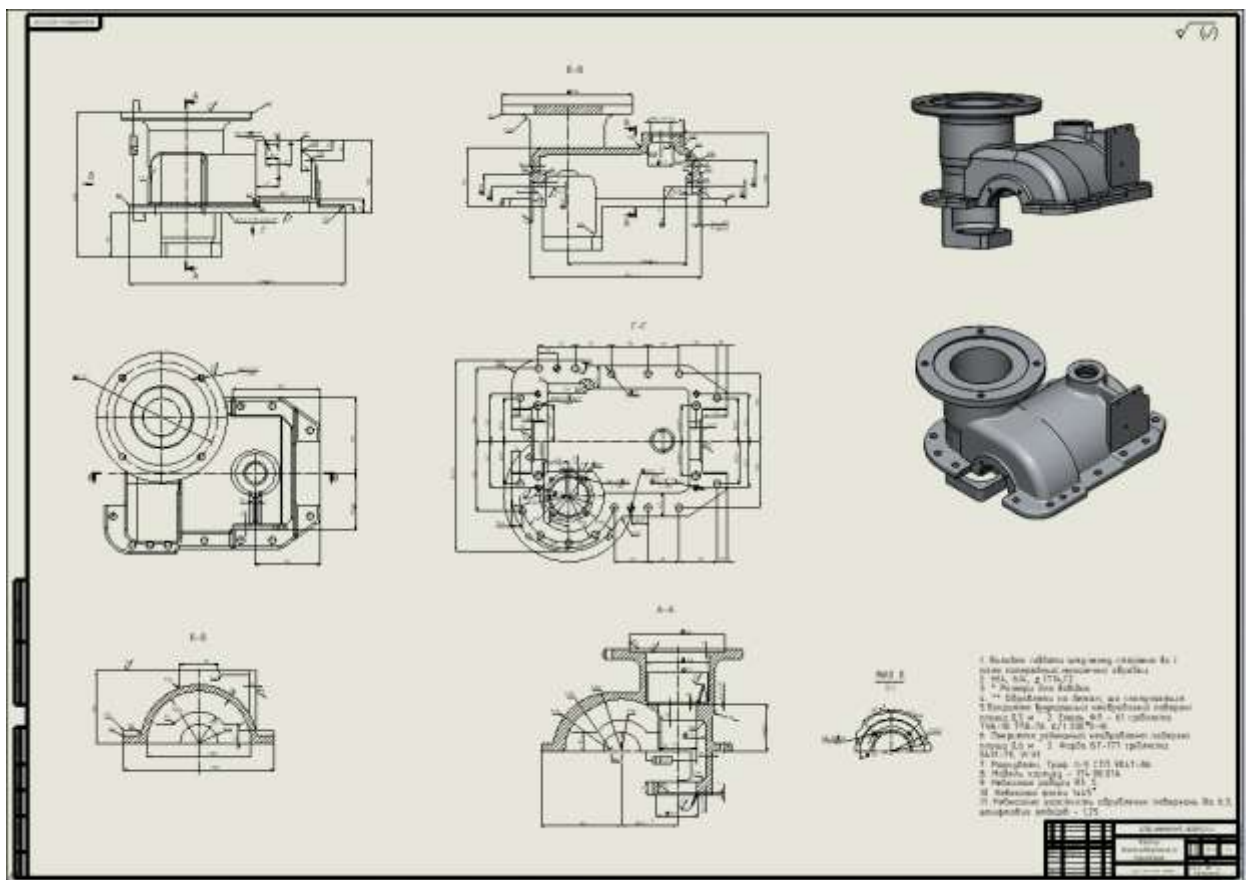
Кресленик деталі «Корпус валоповоротного пристрою»
